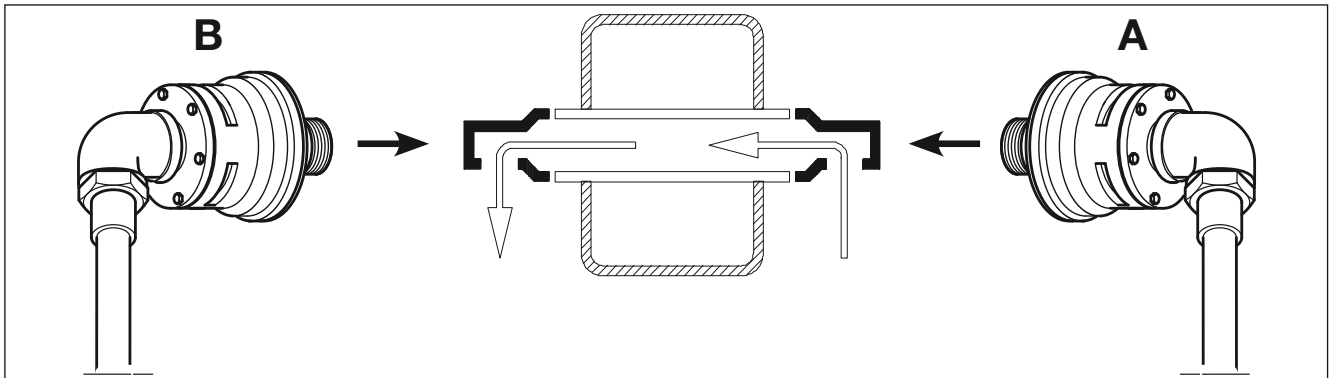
Schema versione ad un passaggio (installazione esterna)
